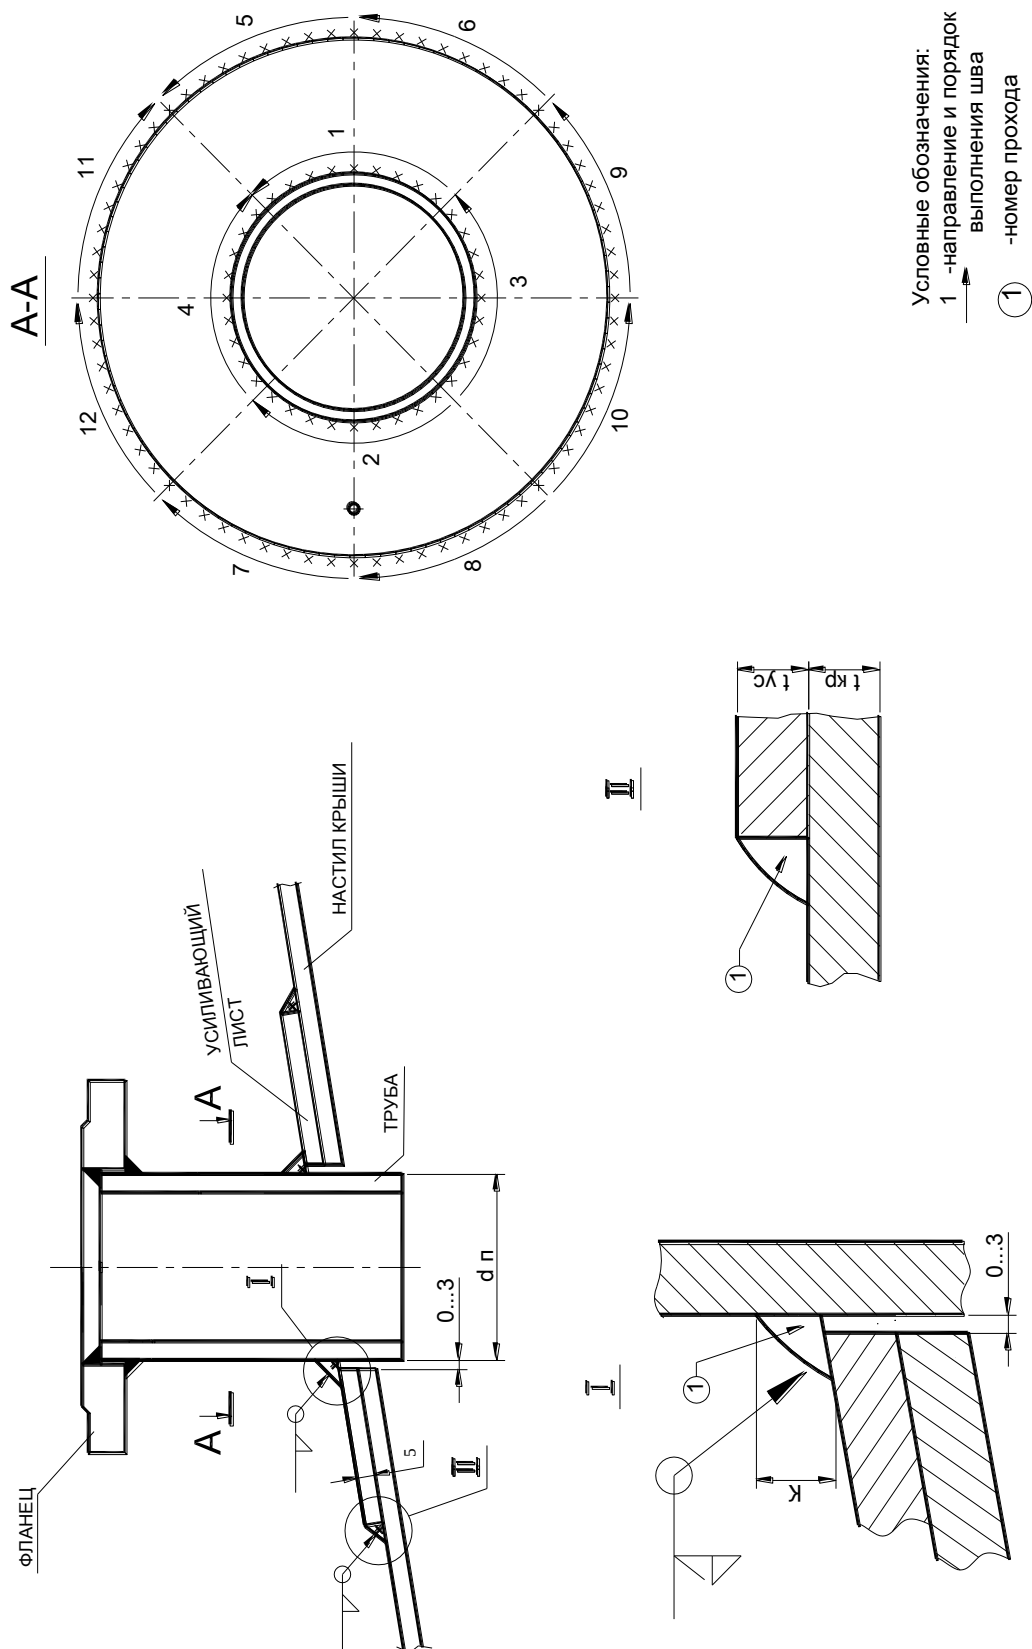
Схема сварки патрубка вентиляционного
